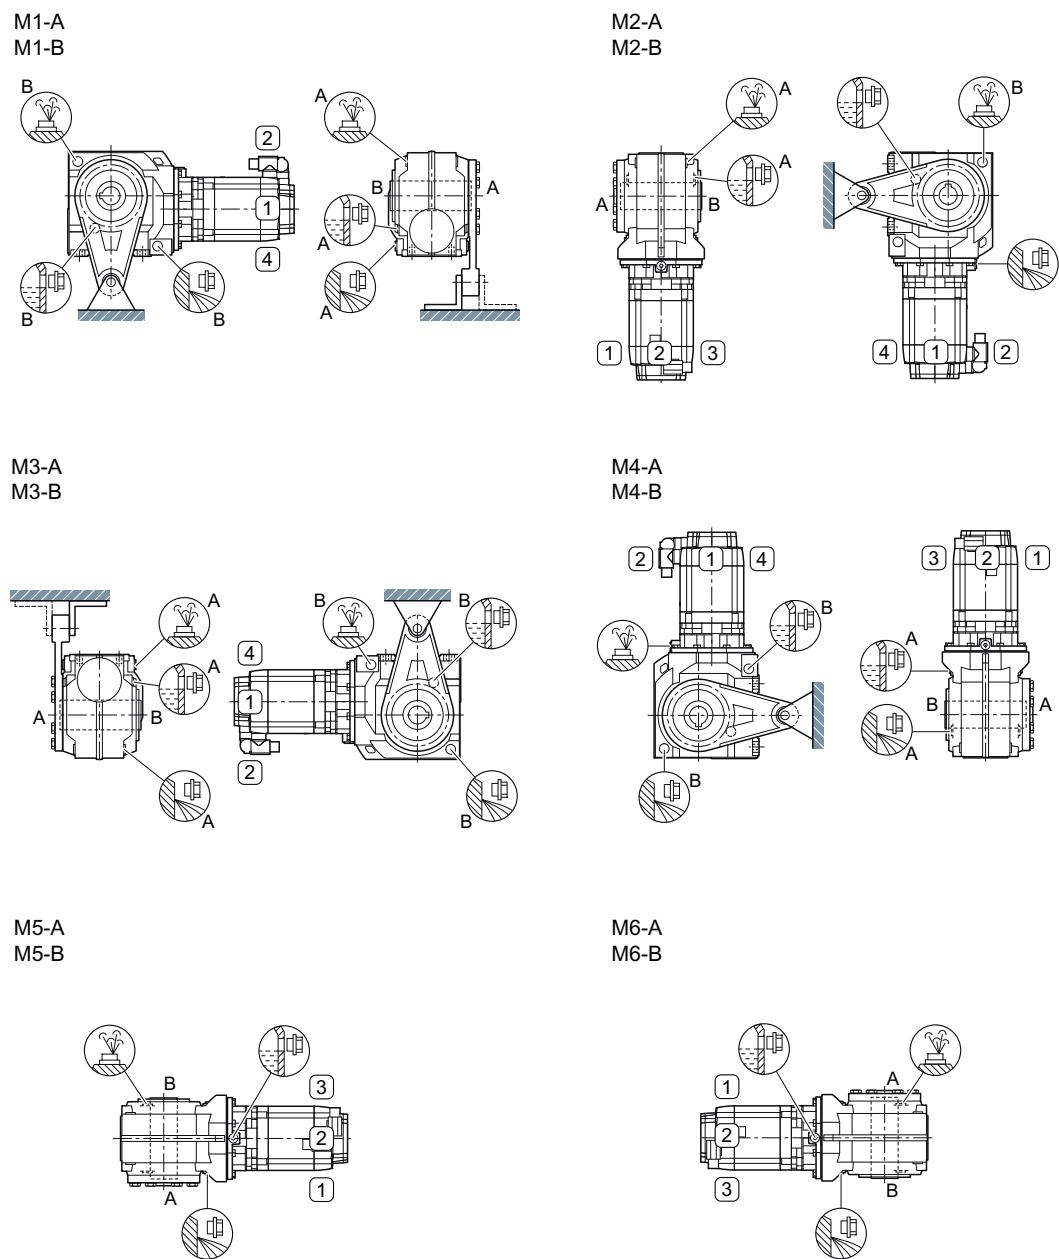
Einbaulagen für Servo-Stirnrad-Schneckengetriebemotor CAD, Aufsteckausführung, Baugrößen 49 - 89, 2-stufig
